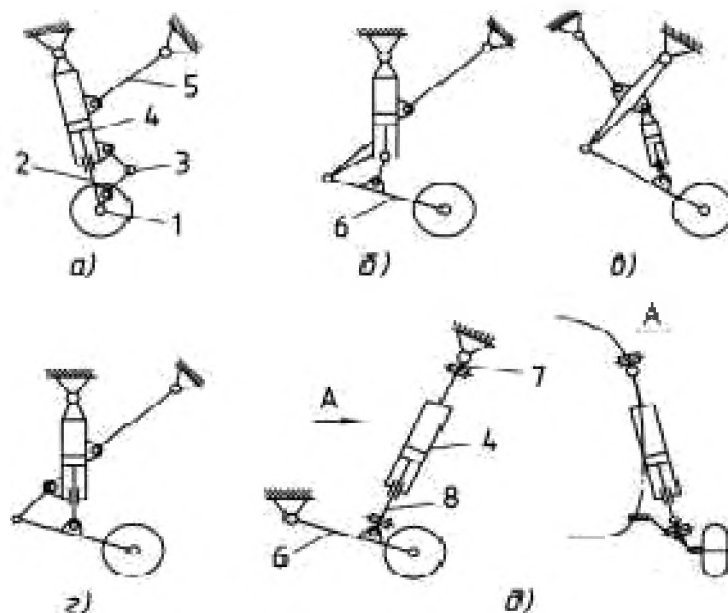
Силовые схемы балочного и рычажного шасси [4]: а- балочная; б,в,г-рычажные; 1-ось колеса, 2-шток амортизатора, 3-шлиц-шарнир, 4-амортизатор, 5-подкос (или цилиндр уборки шасси), 6-рычаг, 7,8-карданные узлы.
